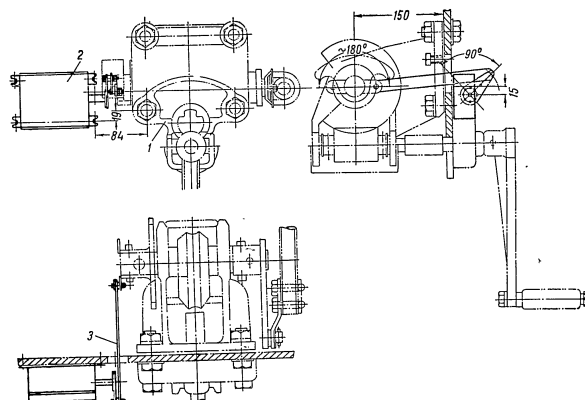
Установка блокконтактов КСА с червячным приводом типа ПЧ-50 для трехполосных разъединителей типа РВУ:
